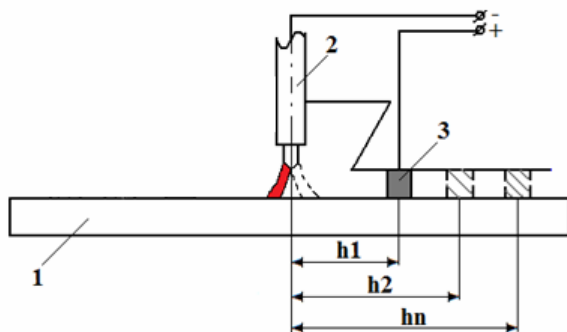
Расположение токоподвода: 1 – стальная пластина; 2 – сварочная горелка; 3 – токоподвод
